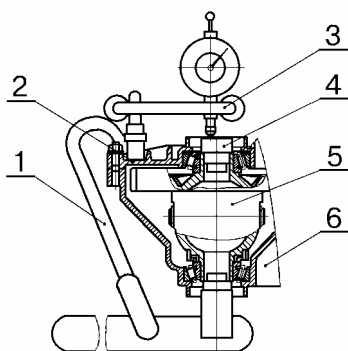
Определение толщины регулировочного кольца подшипника дифференциала:
